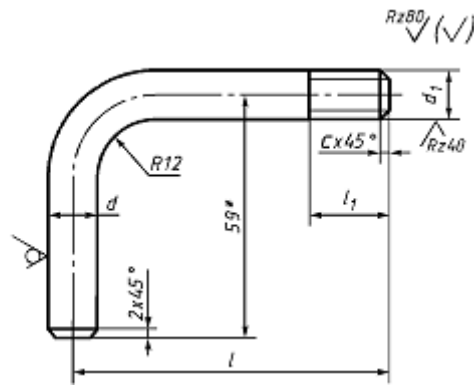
Сварная ручка для стержневого ящика
